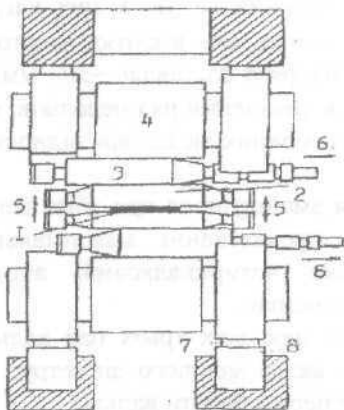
Схема шестивалкової кліті: 1 – штаба; 2 – робочий валок; 3 – проміжний валок; 4 – опорний валок; 5 – напрям дії вигину робочих валків; 6 – напрям осьового переміщення; 7 – месдоза; 8 – гідроциліндр нажимного пристрою.
